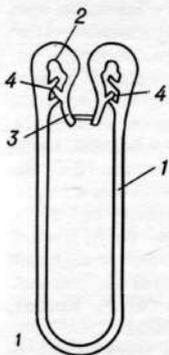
Скрепка (общий вид): 1 — поясок; 2 — захват; 3 — рычажок; 4 — выступ
